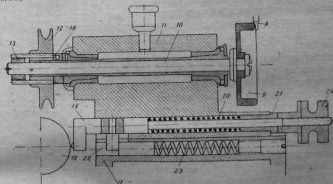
Патрон Квилл для шлифовки и полировки осей баланса.
